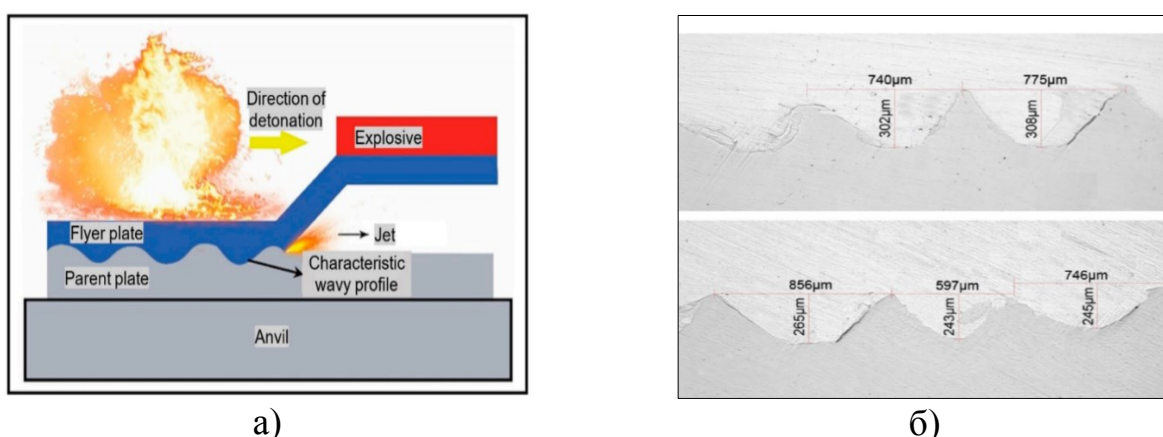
(а) Схема процесса сварки взрывом [125]; (б) Характерная структура сварного соединения после сварки взрывом на примере биметалла медь/нержавеющая сталь [126]
